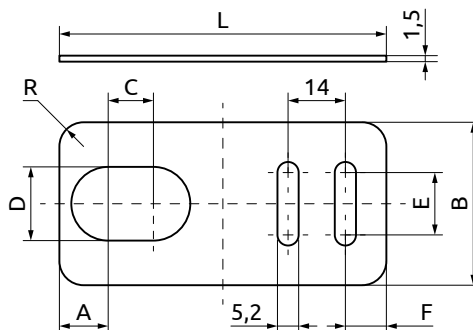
Габаритные размеры кронштейна HoldA-xx
